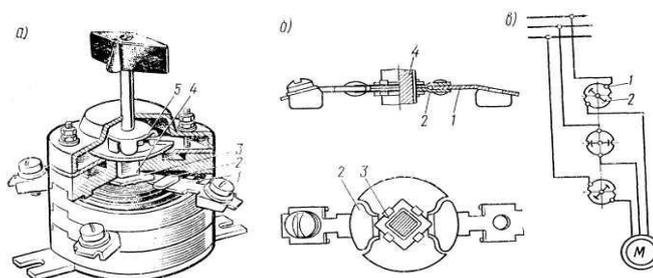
Пакетный выключатель ПВМЗ-25 (а) (разрез по одной его токоведущей цепи (б) и схема присоединения электродвигателя к сети через пакетный выключатель (в))
